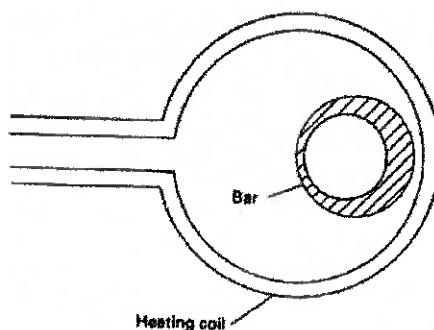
Padrão de aquecimento (hachura) em uma barra cilíndrica posicionada fora de centro [5:172]
